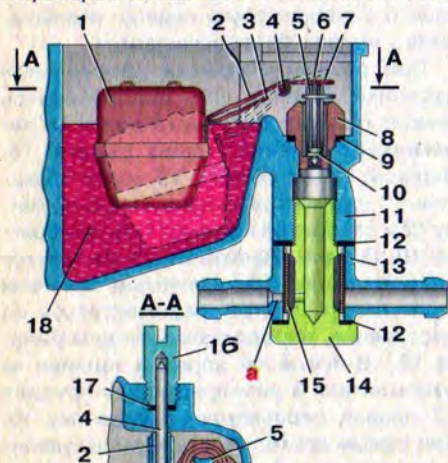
Схема поплавкового механизма и топливоприемной системы: 1 – поплавок; 2 – кронштейн поплавка; 3 – ограничитель хода поплавка; 4 – ось поплавка; 5 – запорная игла топливного клапана; 6 – серьга запорной иглы; 7 – язычок кронштейна для регулировки уровня топлива; 8 – седло топливного клапана; 9, 12, 17 – уплотнительные прокладки; 10 – уплотнительная шайба запорной иглы; 11 – корпус карбюратора; 13 – блок штуцеров подвода и слива топлива; 14 – топливоподающий винт; 15 – топливный фильтр; 16 – пробка-заглушка оси поплавка; 18 – поплавковая камера; а – калиброванное отверстие штуцера обратного слива
